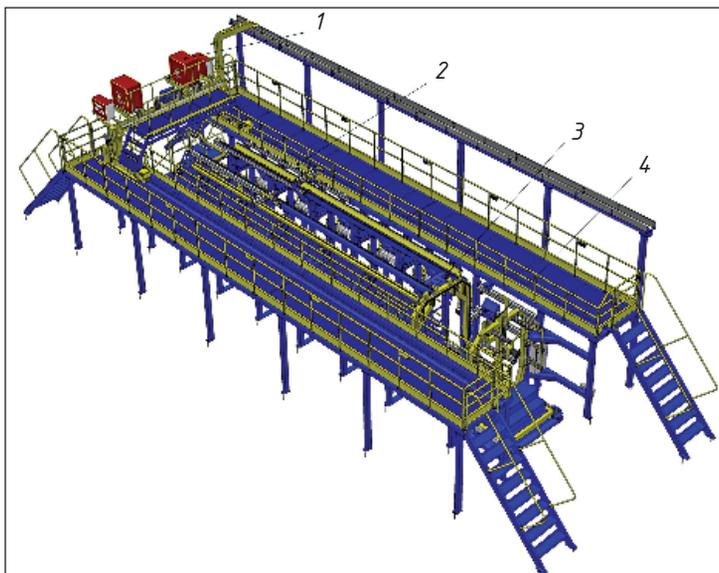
Универсальный перенастраиваемый стенд сборки кузова самосвала
